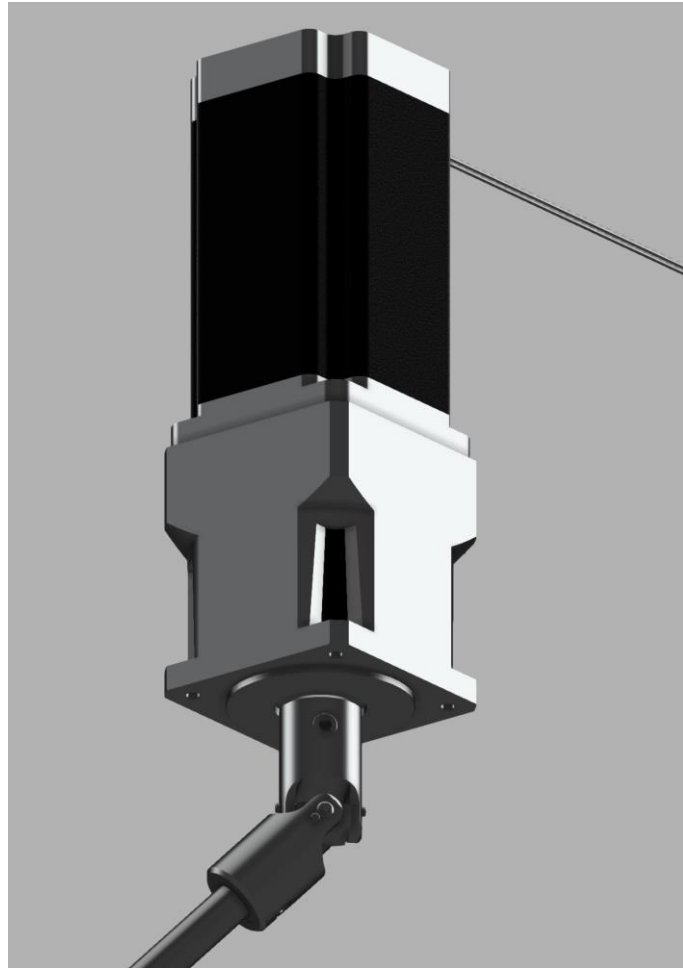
Загальний вигляд крокового двигуна «Nema 34» та редуктору
